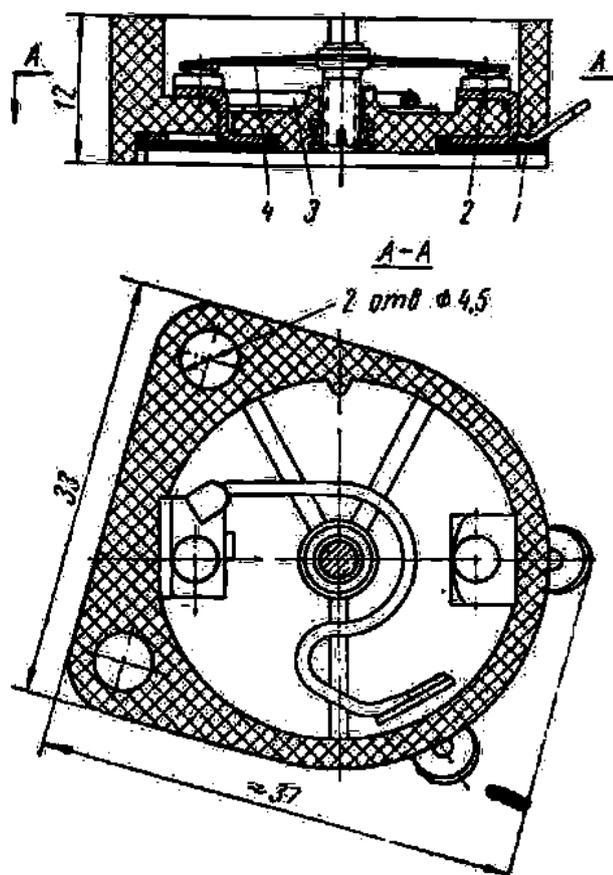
Температурно-токовое реле типа РТ-10: 1- корпус; 2 - пластина контактная; 3 - нагреватель; 4 - термоэлемент
